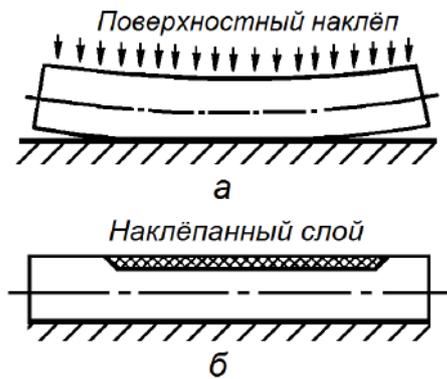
Схема правки прогиба детали наклепом:
